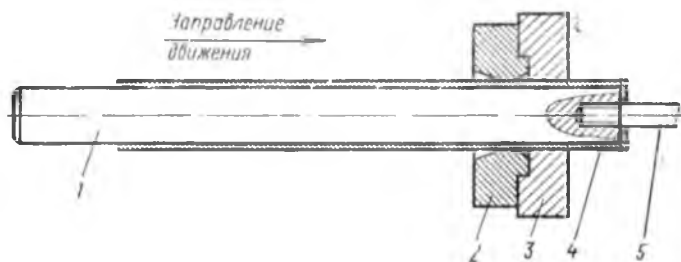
Схема получения заготовки гофрированного волновода:
